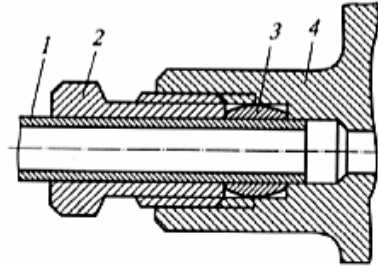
Соединение трубопровода с помощью конусной муфты: 1 – трубка; 2 – упорная гайка; 3 – конусная муфта; 4 – корпус
